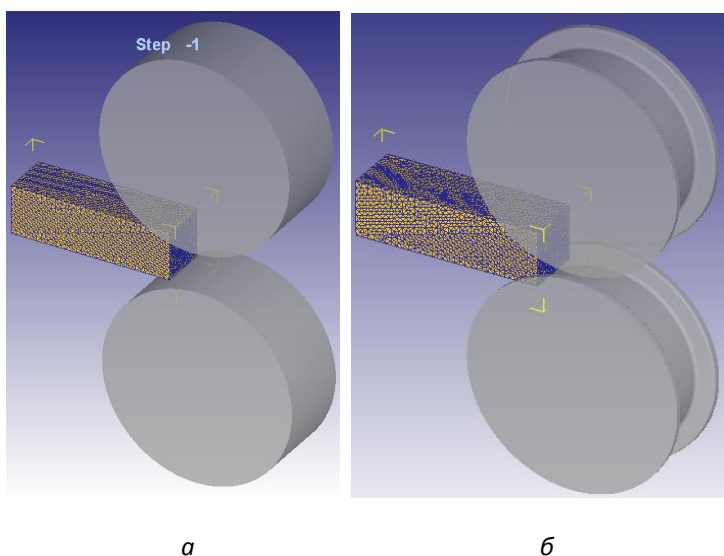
Геометрическая модель прокатки непрерывнолитой заготовки с дефектами макроструктуры в гладких валках (а) и в прямоугольном калибре (б)
